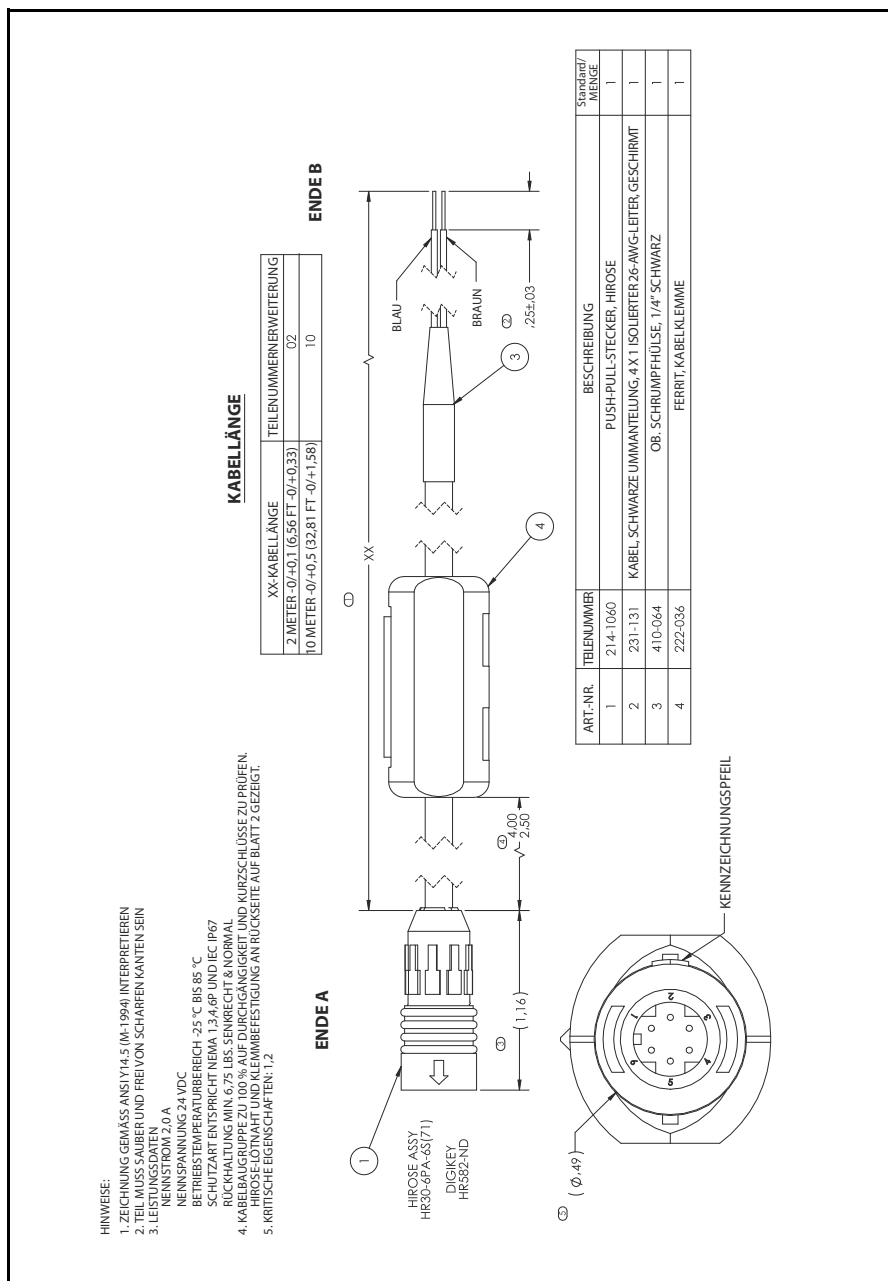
Kabel, Standard (siehe Zeichnung 704-1317, Blatt 1 von 2)
